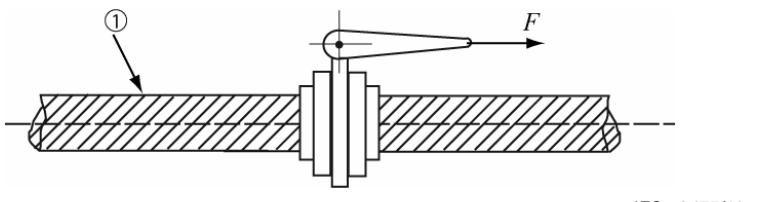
Essai de traction de la vis d'assemblage pour manchons accouplés5.5.2.15 Collier à étrier5.5.2.15.1 Essai de glissement
